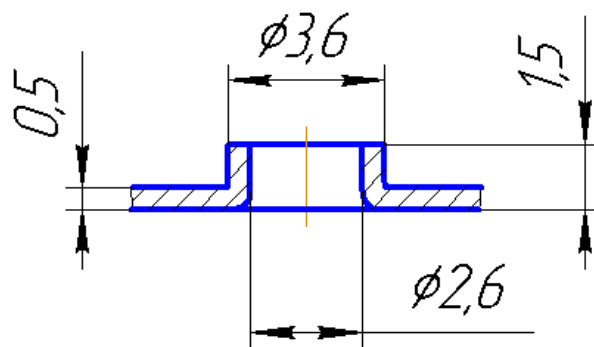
Вариант исполнения разбортовки в листовом металле толщиной 0,5 мм под самонарезающий винт диаметром 3,2 мм по DIN 7981 с различными инструментами форм
